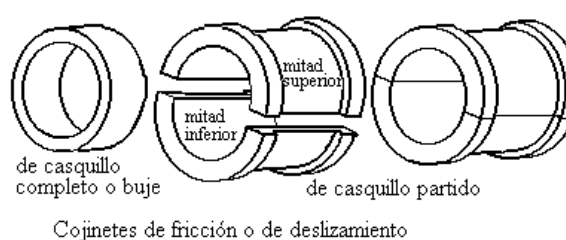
COJINETES DE DESLIZAMIENTO
